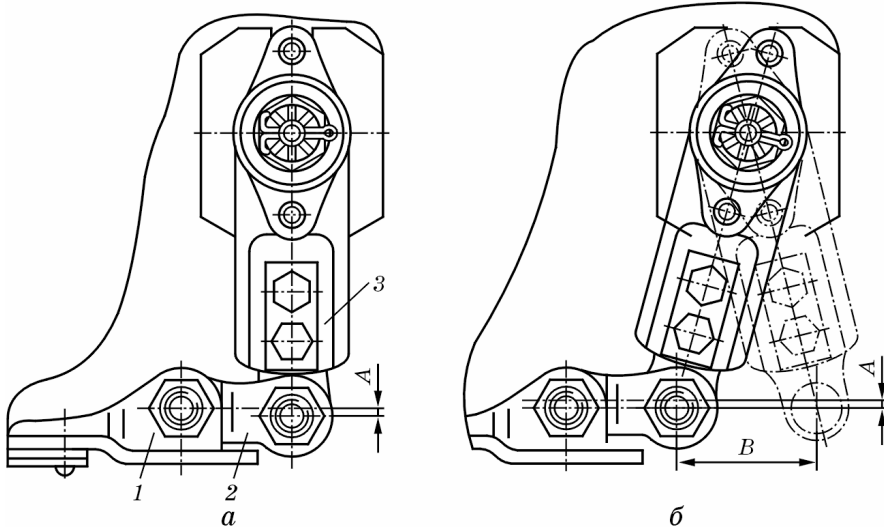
Регулювання з'єднання головок ножа і важеля механізму коливальної шайби:
